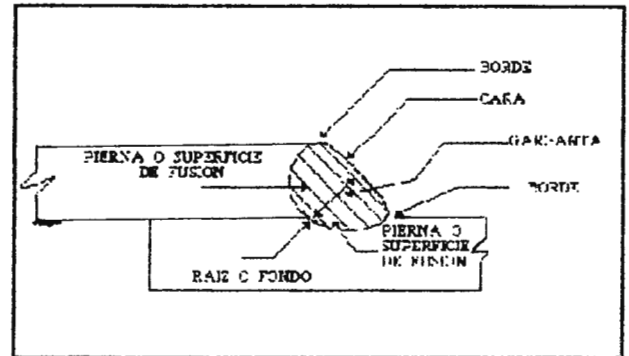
Términos comunes aplicados a una soldadura
